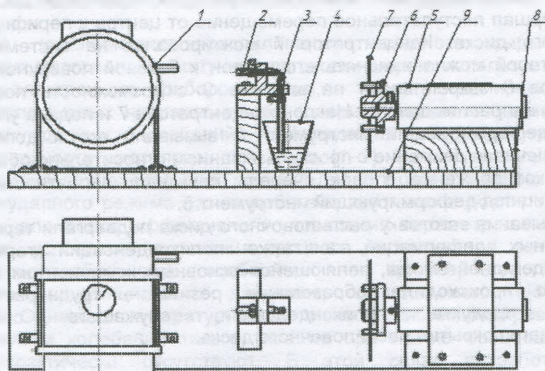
Схема установка для напыления абразивных зерен на боковую поверхность распиловочных дисков
